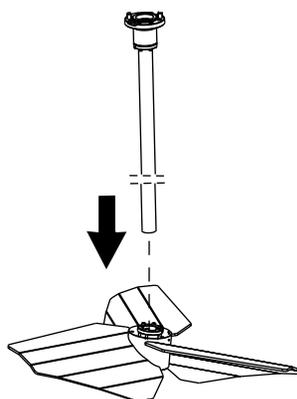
Трехлопастный сварной пропеллер с лопастями типа "гидроfoil"
